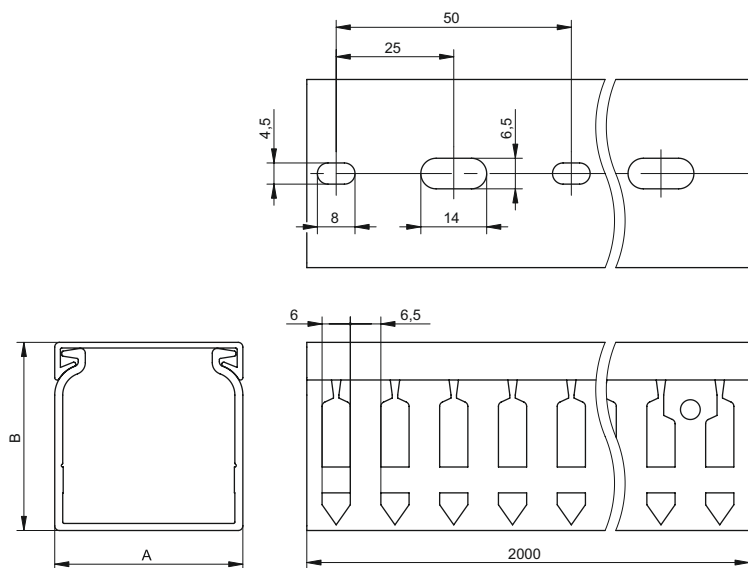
Размеры кабель-канала / Figure 1 – Cable trunking dimensions / 1-сурет – Тесілген кабель-арнасы өлшемдері
